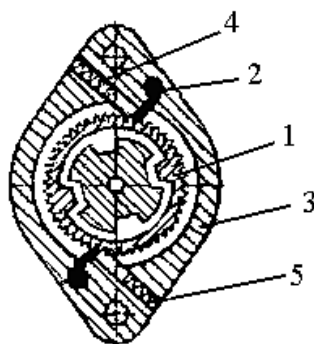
Поворотный механизм с двумя собачками в корпусе.
